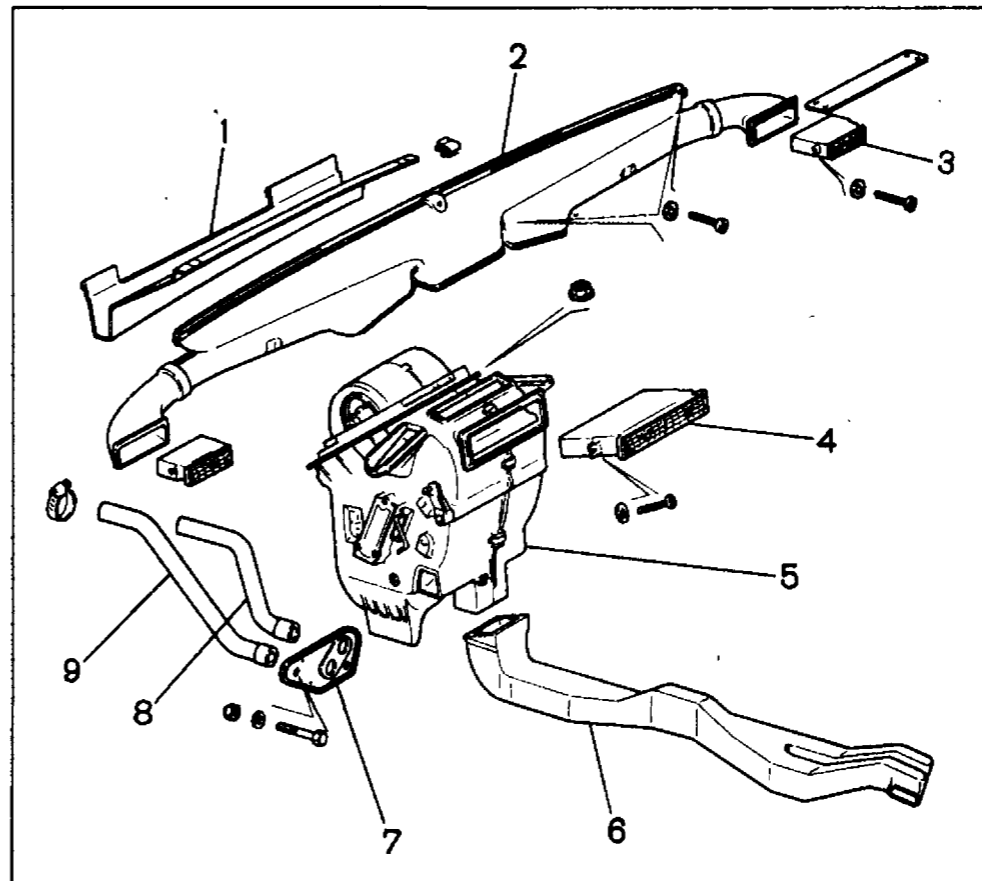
Отопитель с воздухопроводами и соплами вентиляции: 1 — водоотражательный щиток; 2 — воздухопровод обогрева ветрового стекла в сборе с воздухопроводами боковых сопел; 3 — боковое сопло вентиляции салона; 4 — центральное сопло вентиляции салона; 5 — отопитель в сборе; 6 — воздухопровод внутренней вентиляции; 7 — уплотнитель труб крана отопителя; 8 — отводящий задний шланг отопителя; 9 — подводящий задний шланг отопителя
